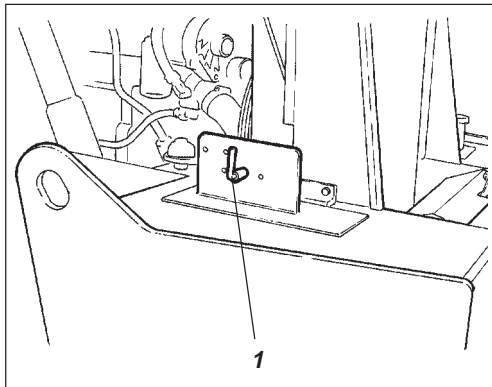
Bastidor de cabeza, lado izquierdo trasero
